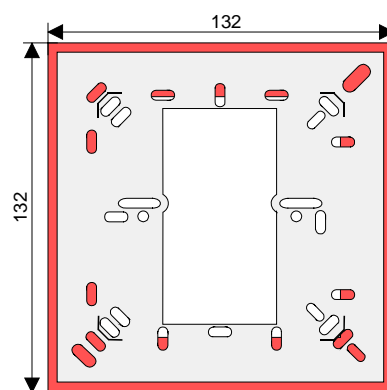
Marco de montaje universal (Art.-Nr. 704967)
